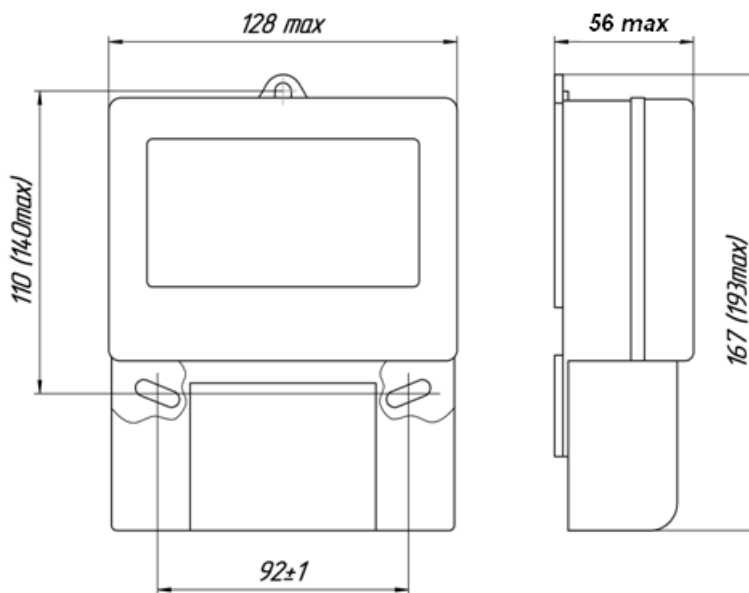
б – Габаритные и установочные размеры ДД РИМ 040.03-02, (-03),(-04)
